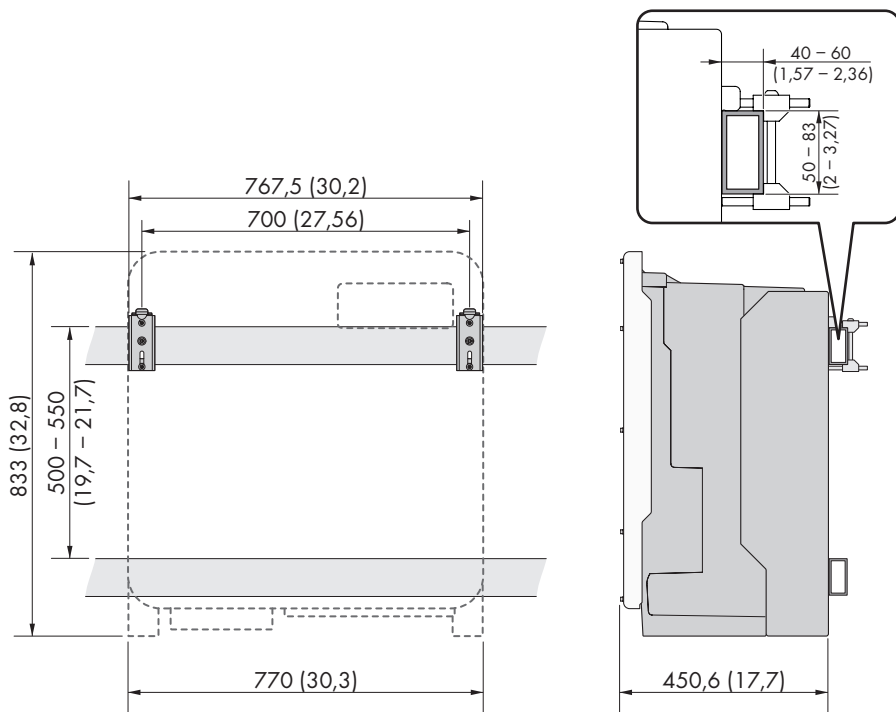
Dimensions des rails profilés et la zone de serrage du support de montage (mesures en mm (in))
